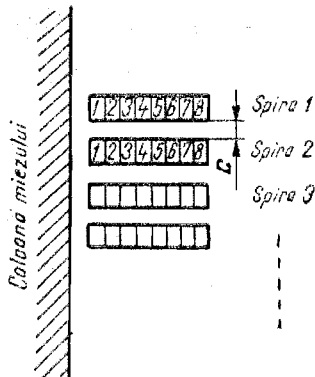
Schemă de bobină spiralată cu 8 conductoare în paralel.
